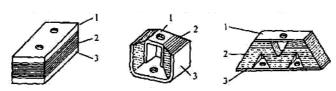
Типовые конструкции резинометаллических виброизоляторов: 1 — верхняя пластина; 2 — резиновый массив; 3 — нижняя пластина
